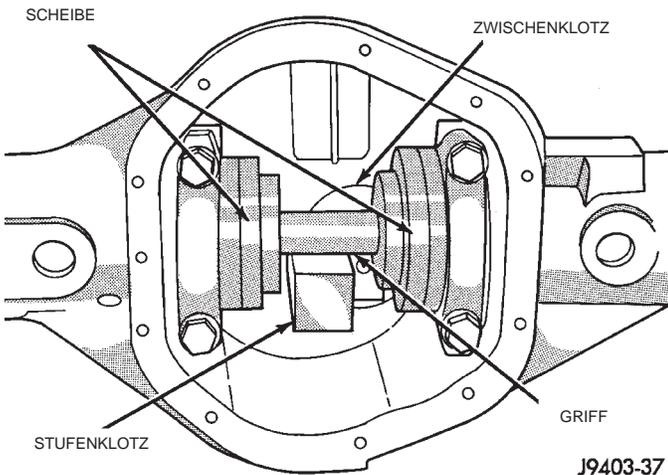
Meßwerkzeuge im Gehäuse eingebaut—Typisch
